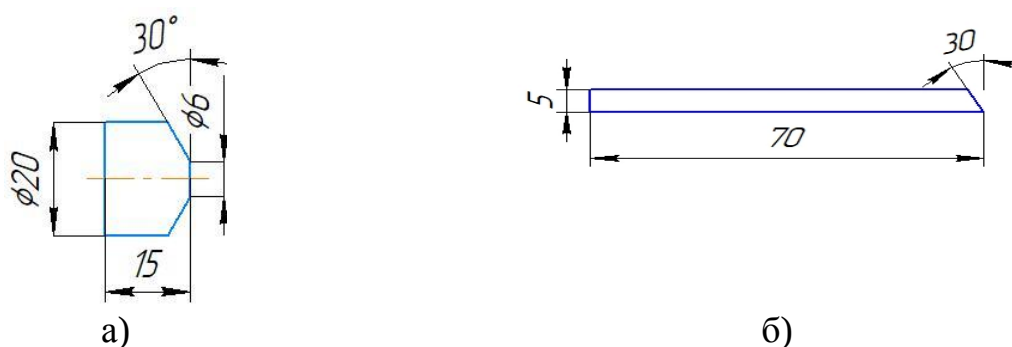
Внешний вид образцов со скосом кромок для исследования свариваемости: а) цилиндрические; б) пластины
